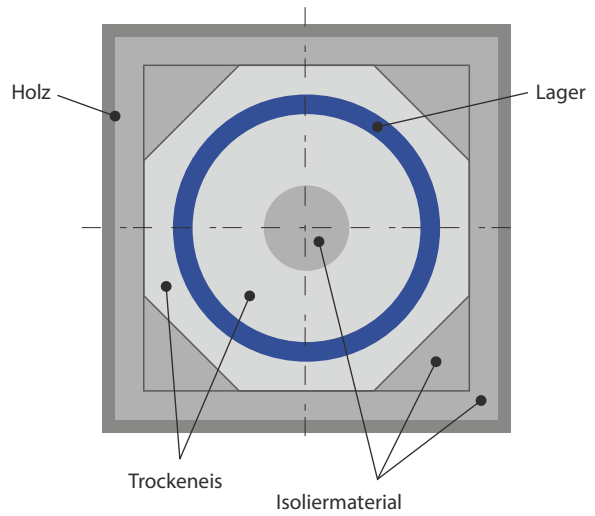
Holzbehälter für Trockeneis (Aufsicht)
